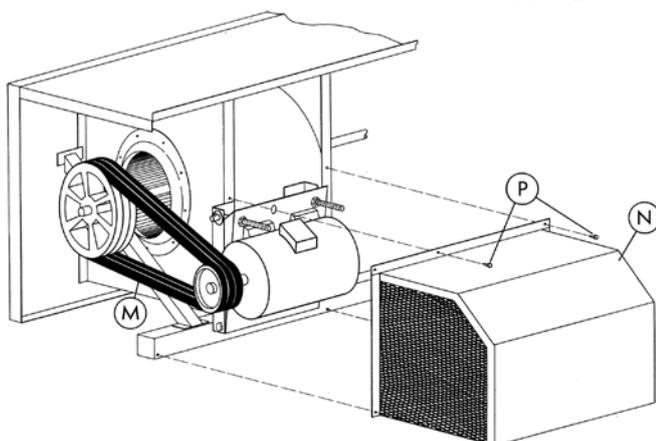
Montage von Motorabdeckung und Keilriemen
